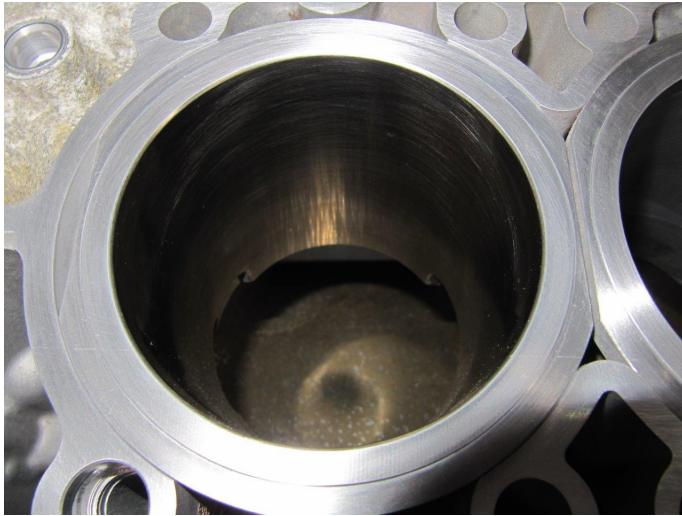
Erneuerter Schmiede-Zylinder mit NiSiC-Beschichtung
